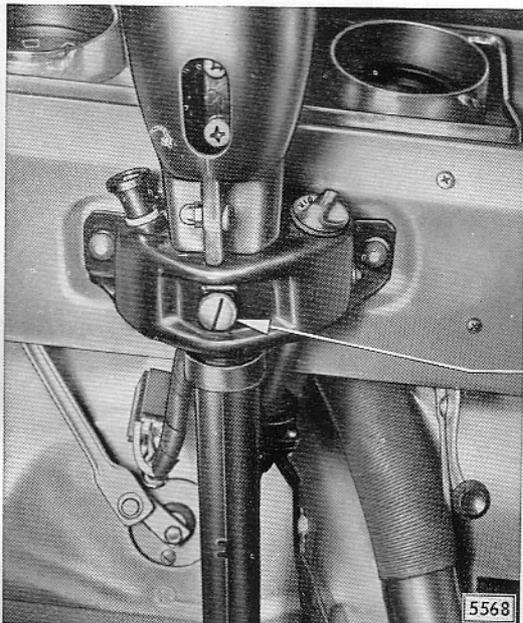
Anschlagschraube für Lenkspindel in Haltebügel für Lenkstützrohr
